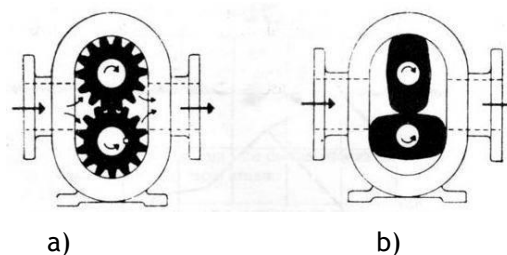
Bombas volumétricas: a) Bomba de engrenagens; b) Bomba de lóbulos
